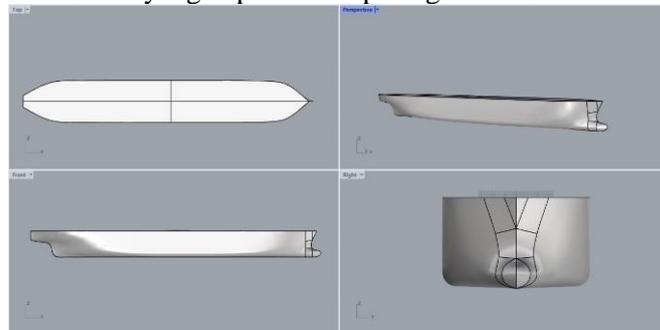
Sheer Plan Kapal Container 4000 TEU
